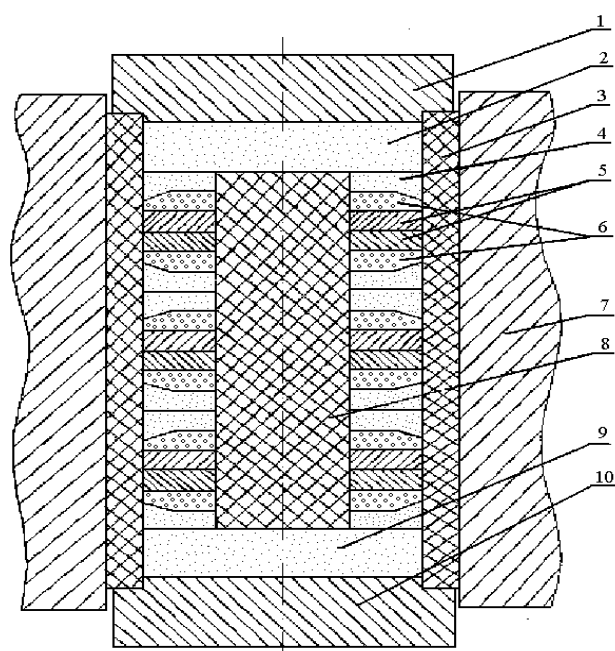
Схема сборки КВД для спекания шлифовальных головок ШГК: 1 – верхний поршень; 2 – торцевой нагреватель; 3 – электро- и теплоизолирующая катлитовая обойма; 4 – графитовый диск; 5 – стальной корпус; 6 – алмазная шихта; 7 – контейнер высокого давления; 8 – катлитовый стержень; 9 – торцевой нагреватель; 10 – нижний поршень
